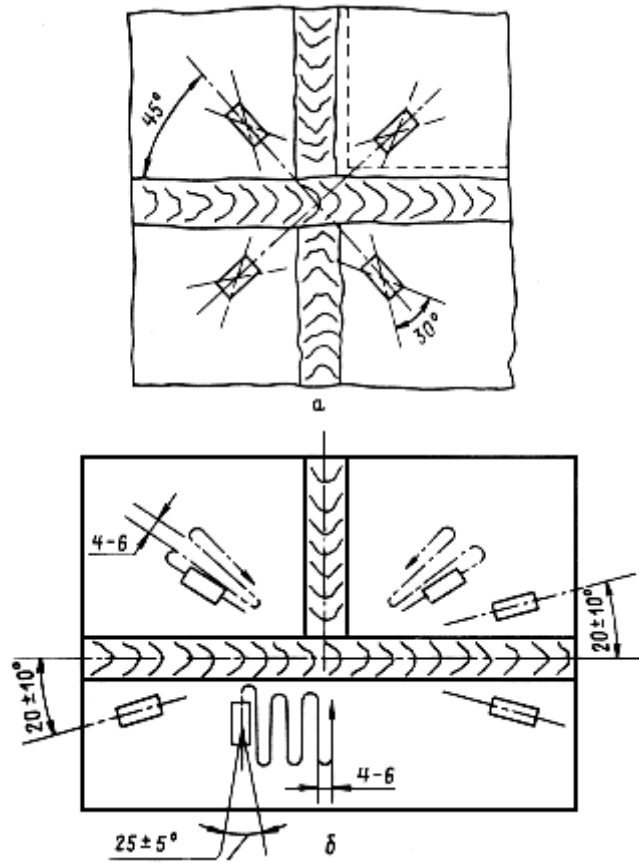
Схема сканирования при ультразвуковом контроле пересечений (а) и сопряжения (б) сварных швов
